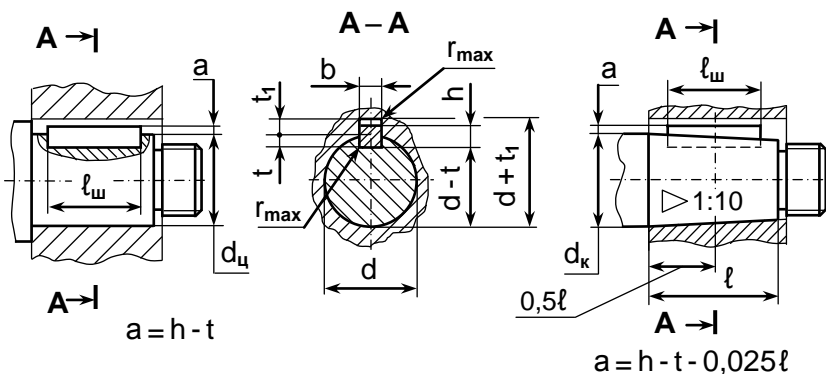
Соединение конца вала с призматической шпонкой по ГОСТ 23360 – 78 (таблица Е.14)
